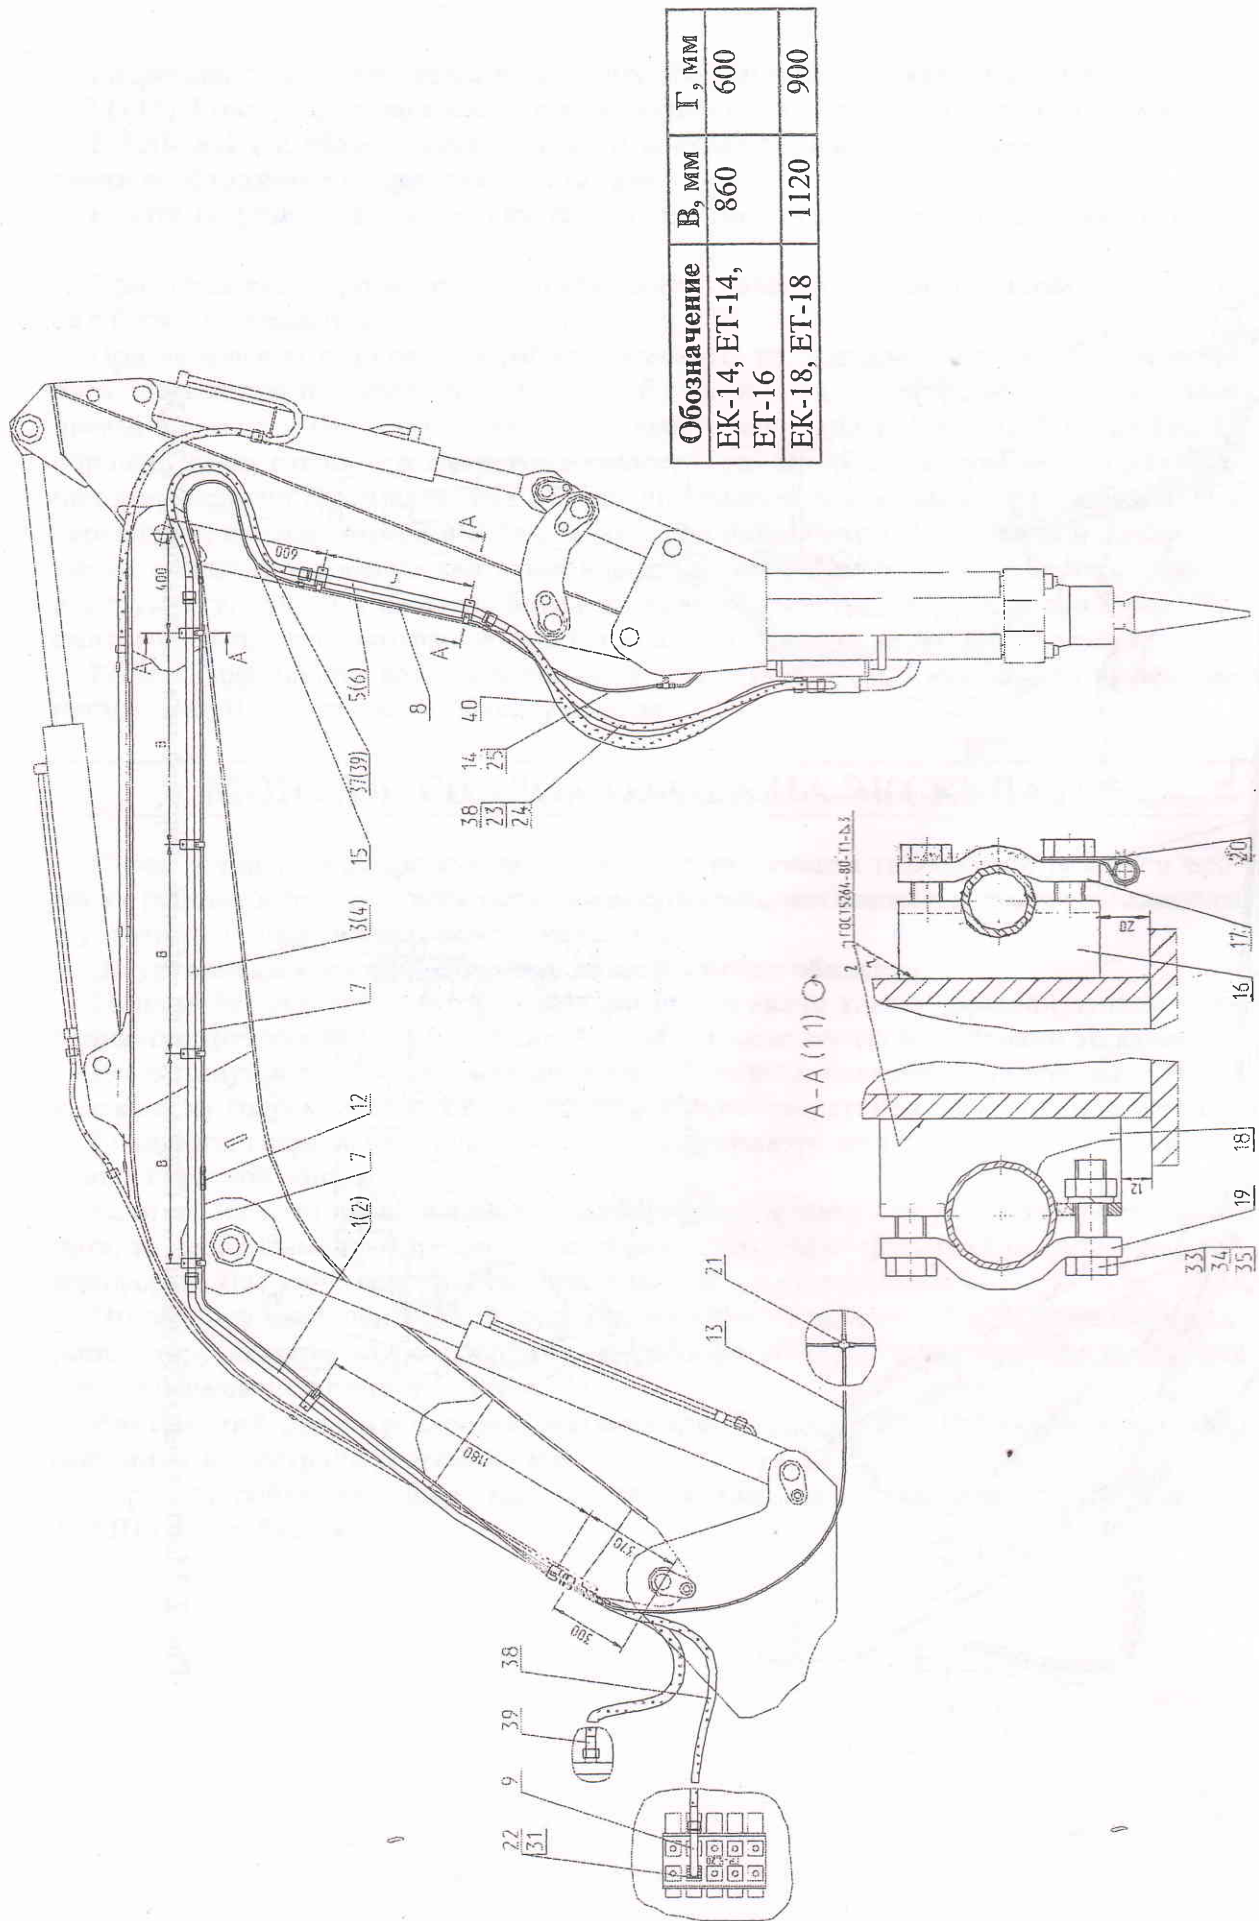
Монтаж гидрооборудования гидромолота на рабочем оборудовании экскаваторов ЕК-14, ЕТ-14, ЕТ-16, ЕК-18, ЕТ-18
